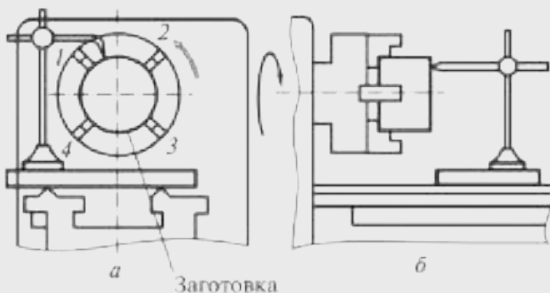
Закріплення та вивірка заготовки за допомогою рейсмуса та креслярки: а — рейсмусом по зовнішній поверхні; б — рейсмусом по торцю; 1, 2, 3, 4 — номери кулачків патрона
